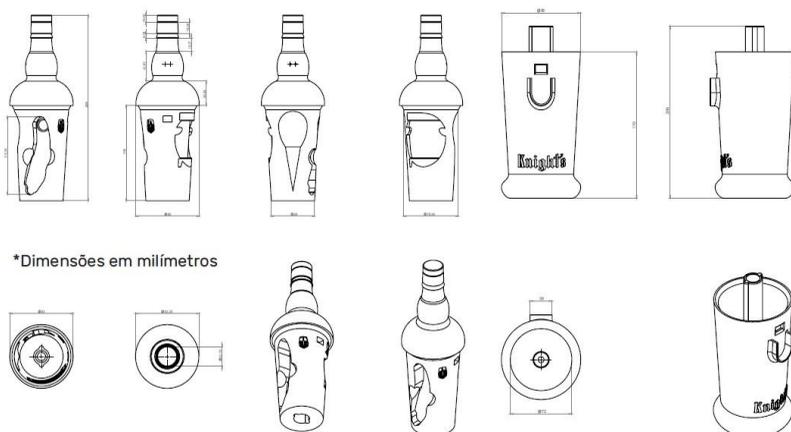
Desenho técnico da garrafa/kit para vinho de Porto
